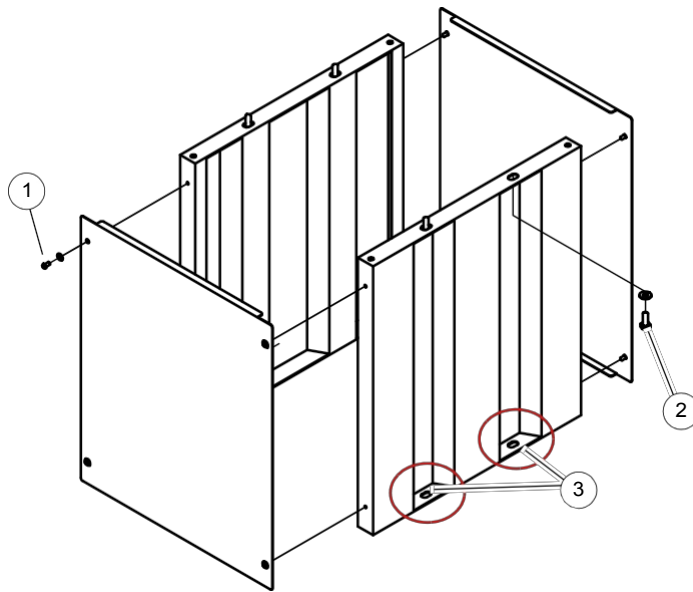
Schéma d'assemblage du bâti de la machine
